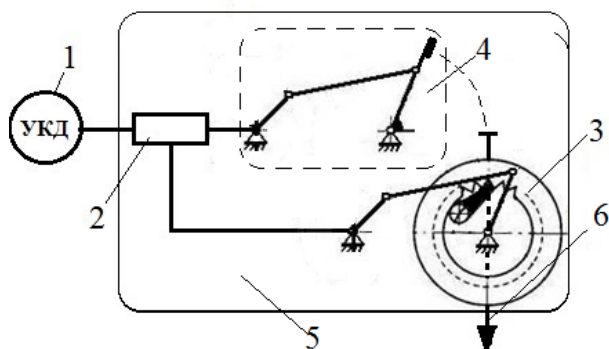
Структурная схема перфоратора ударно-поворотного действия: 1 - универсальный коллекторный двигатель; 2 - редуктор; 3 - поворотный механизм; 4 - ударный механизм; 5 - ударно-поворотная система; 6 - инструмент
